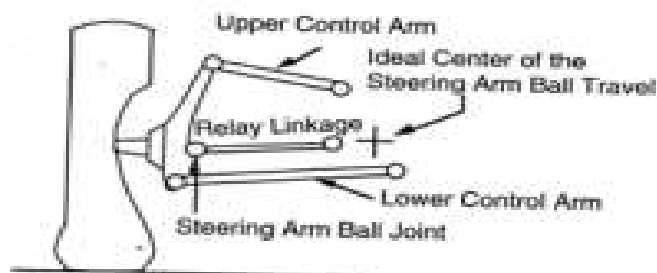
Erreur de géométrie causant de la prise de pince / ouverture
